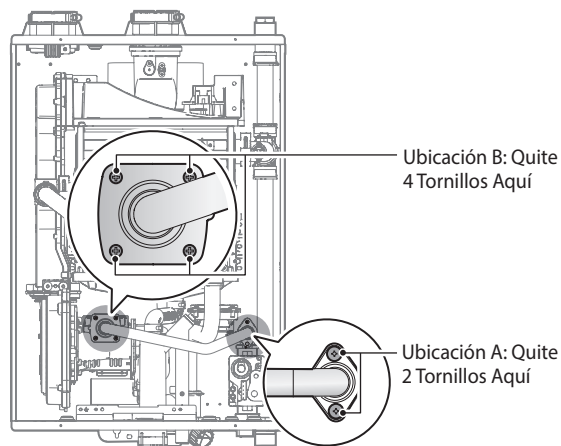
Separación de la Válvula de Gas del Tubo de Entrada de Gas y el Conjunto del Motor del Ventilador
